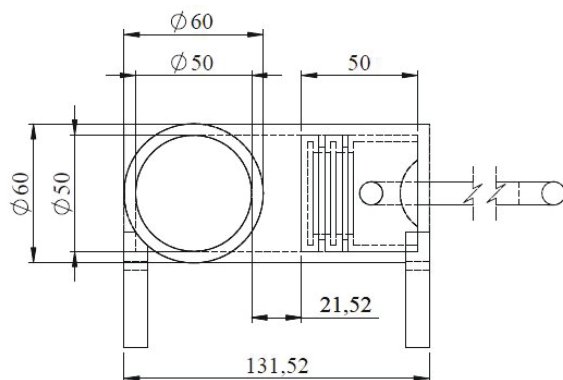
Plano del pistón diseñado (dimensiones en mm).
